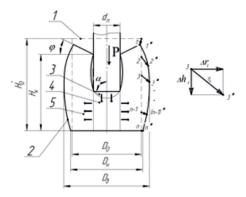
Анализ формоизменения цилиндрической заготовки при открытой прошивке
